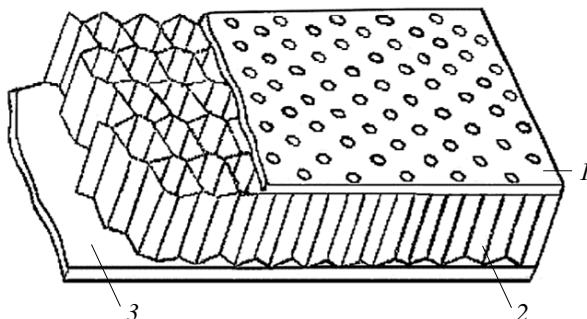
Схематичное изображение однослойной звукопоглощающей конструкции: 1 – перфорированный лист; 2 – сотовый наполнитель; 3 – неперфорированный лист [10]
